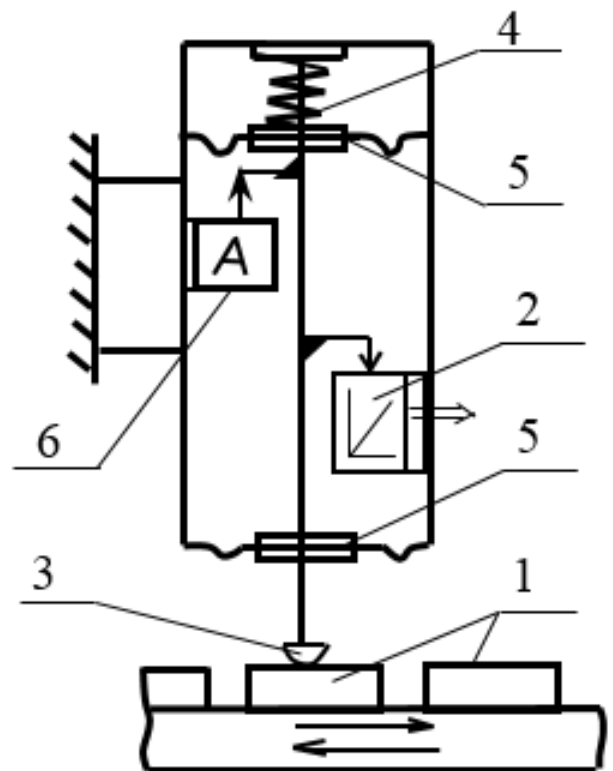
Вимірювальний пристрій для контролю висоти деталей
